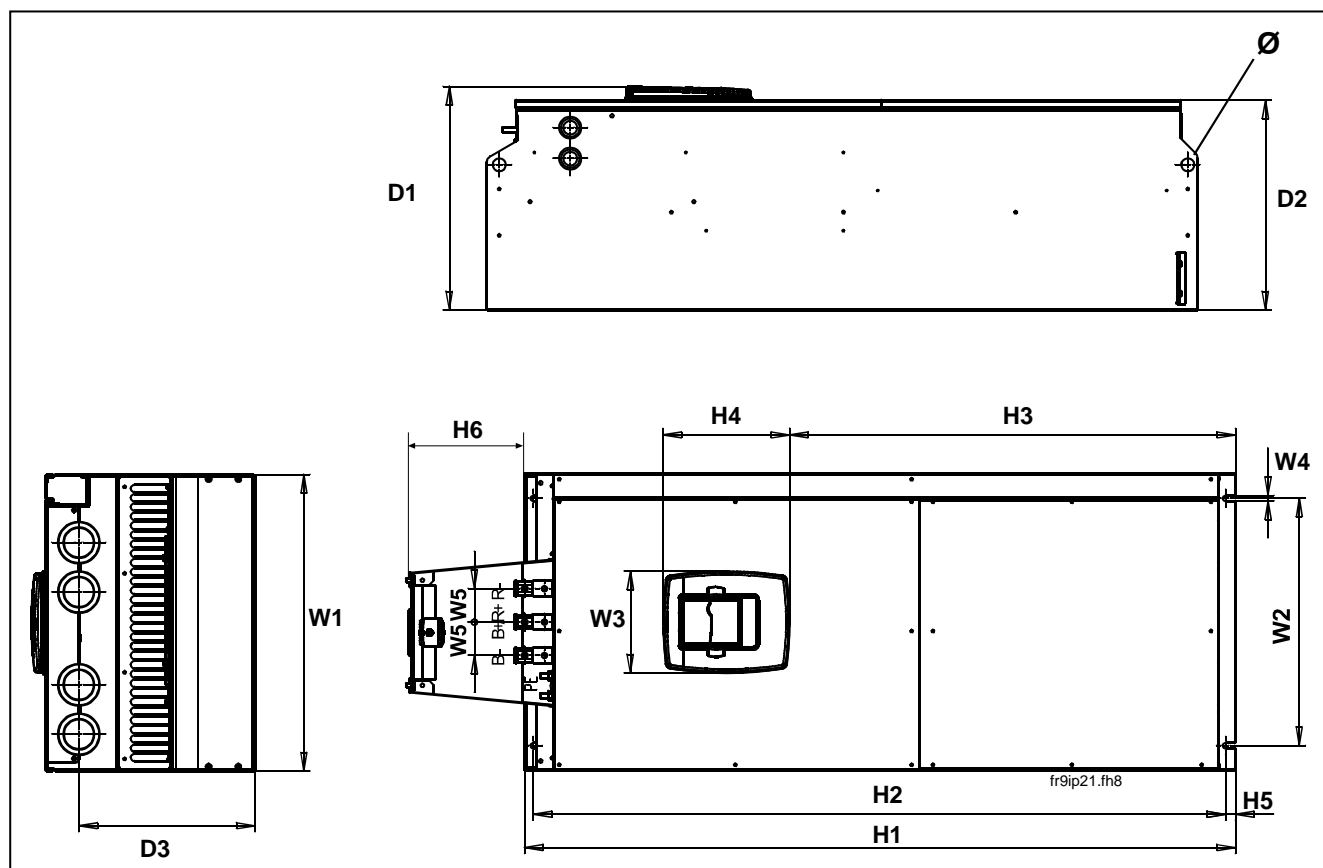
Dimensioni di ingombro dei Vacon NX\_, FR9
